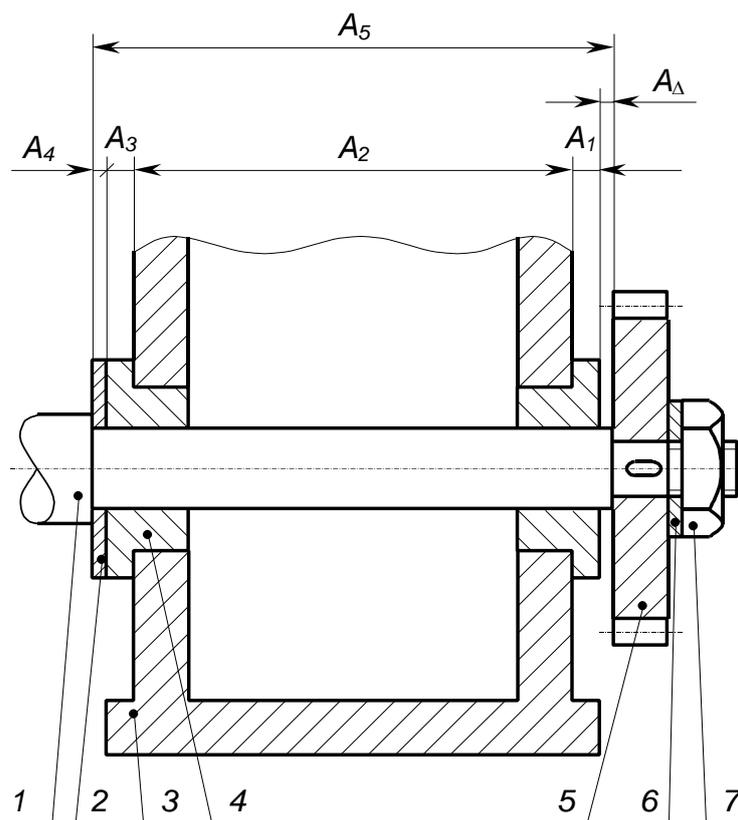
Часть сборочного чертежа механизма:
